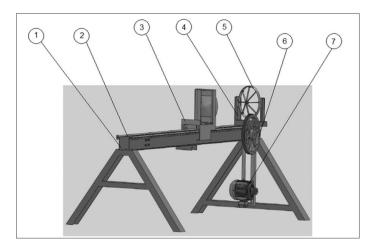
Vista geral da máquina seccionadora e componentes principais: 1) Estrutura, 2) Guias lineares, 3) Carrinho de força, 4) Suporte de fixação da faca, 5) Faca estrela, 6) Sistema de transmissão, 7) Motor.
